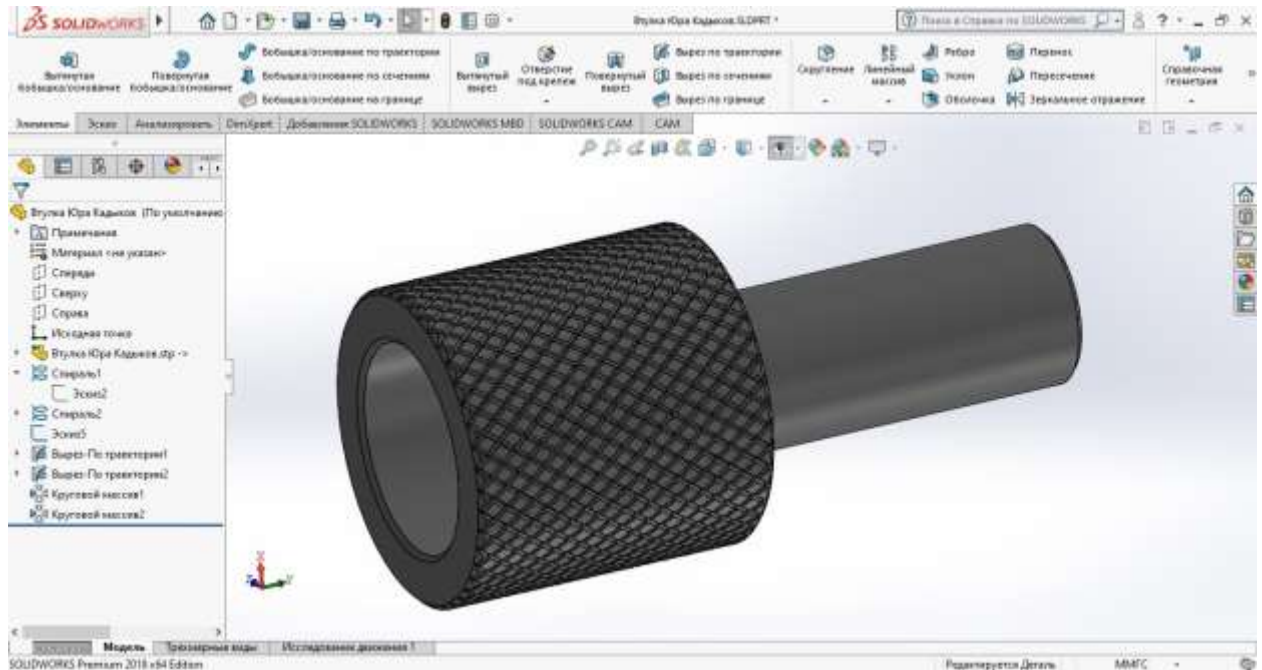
3-D модель деталі «Втулка рифлена» (Вид 1)
